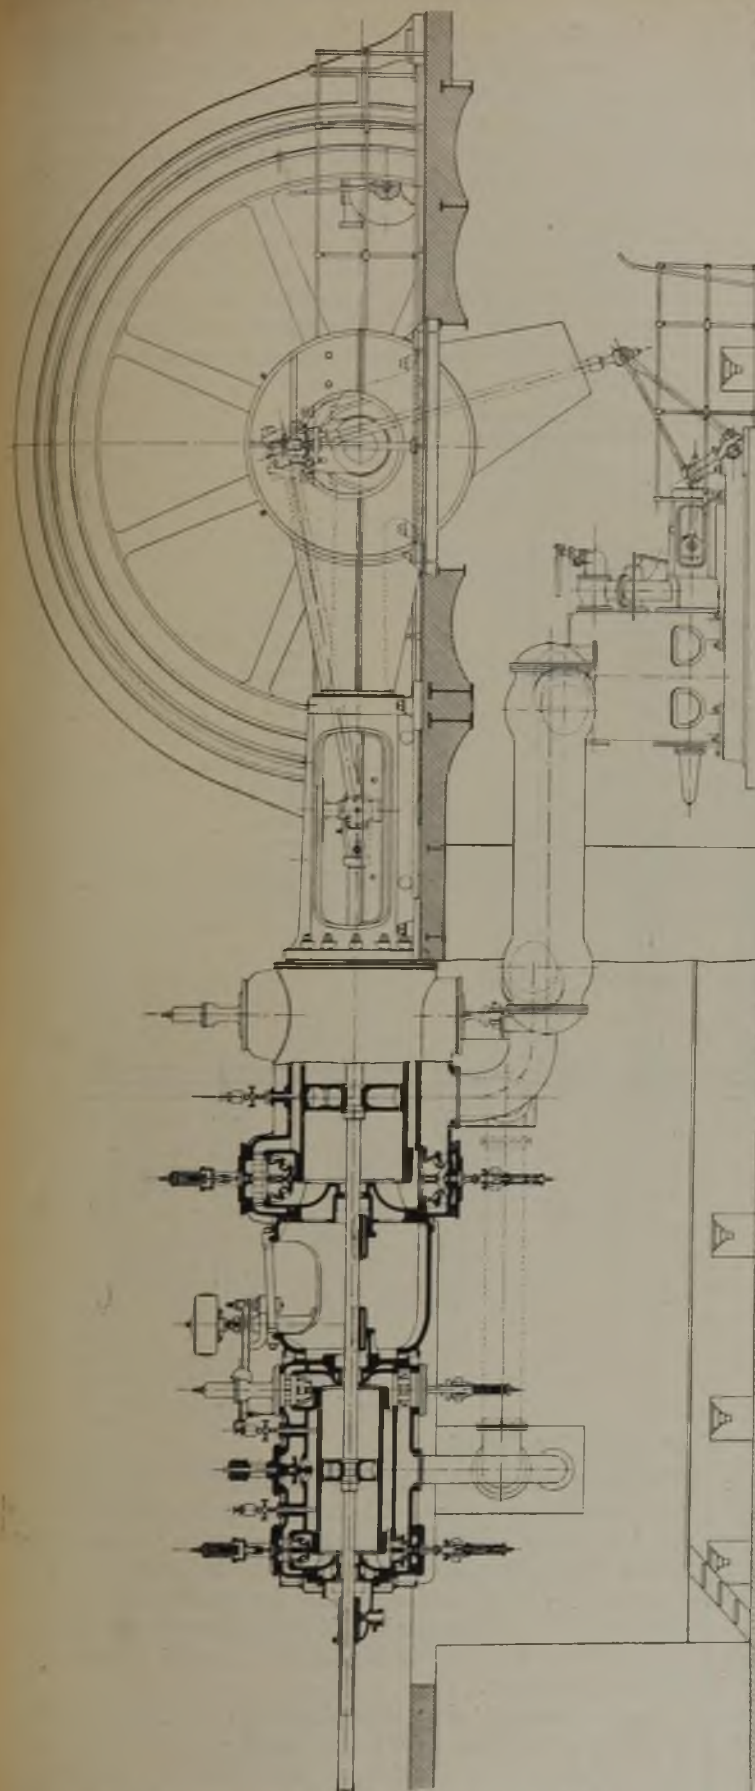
Längsschnitt durch den Hochdruckzylinder einer Generatorenmaschine.
